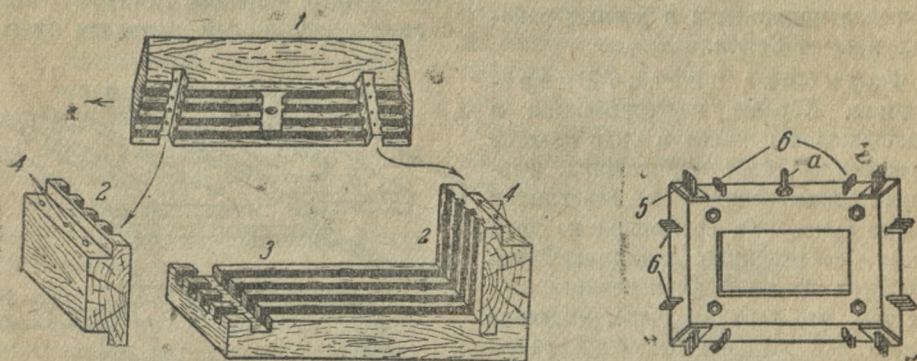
Колodka мундштука и её детали: 1—верхняя стенка, 2—боковые стенки, 3—нижняя стенка, 4—отверстия для болтов, 5 — болты мундштука, 6—отверстия для прочистки канавок мундштука
